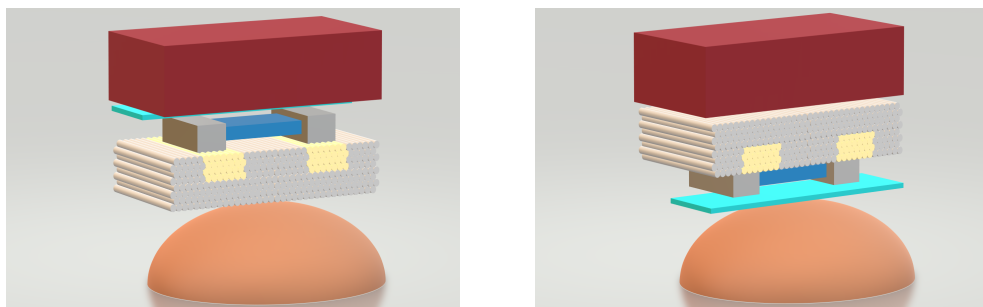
Kontaktování termokompresí - Umístění součástky
